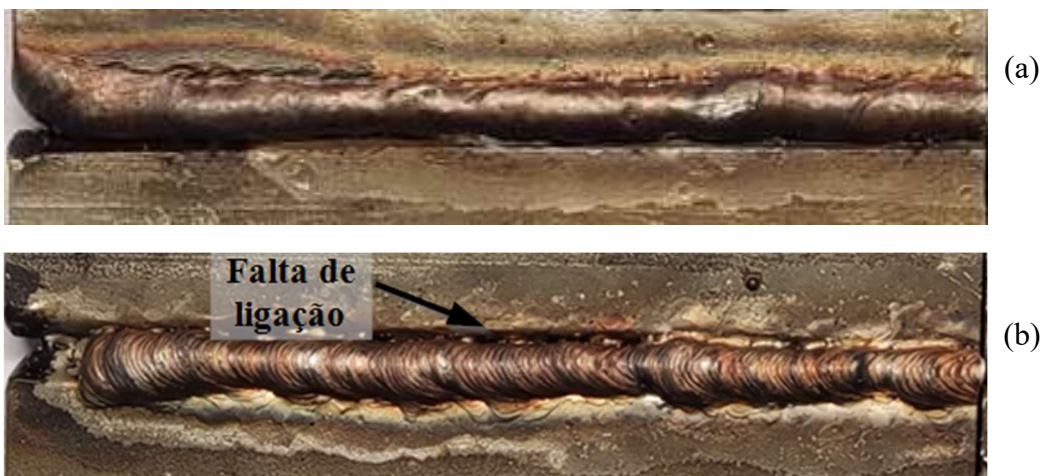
Cordões de soldadura da Amostra F. Primeiro passe (a) e Segundo passe (b).
